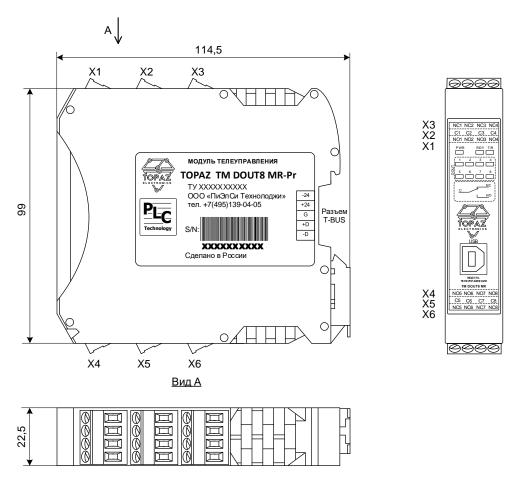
Габаритные размеры модуля TOPAZ TM DOUT8 MR-Pr
